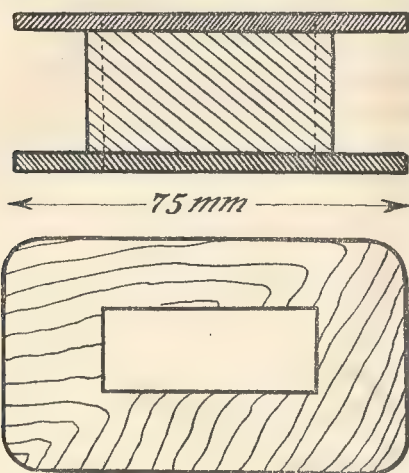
Die Spule für das Voltmeter, Seitenansicht und Draufsicht
